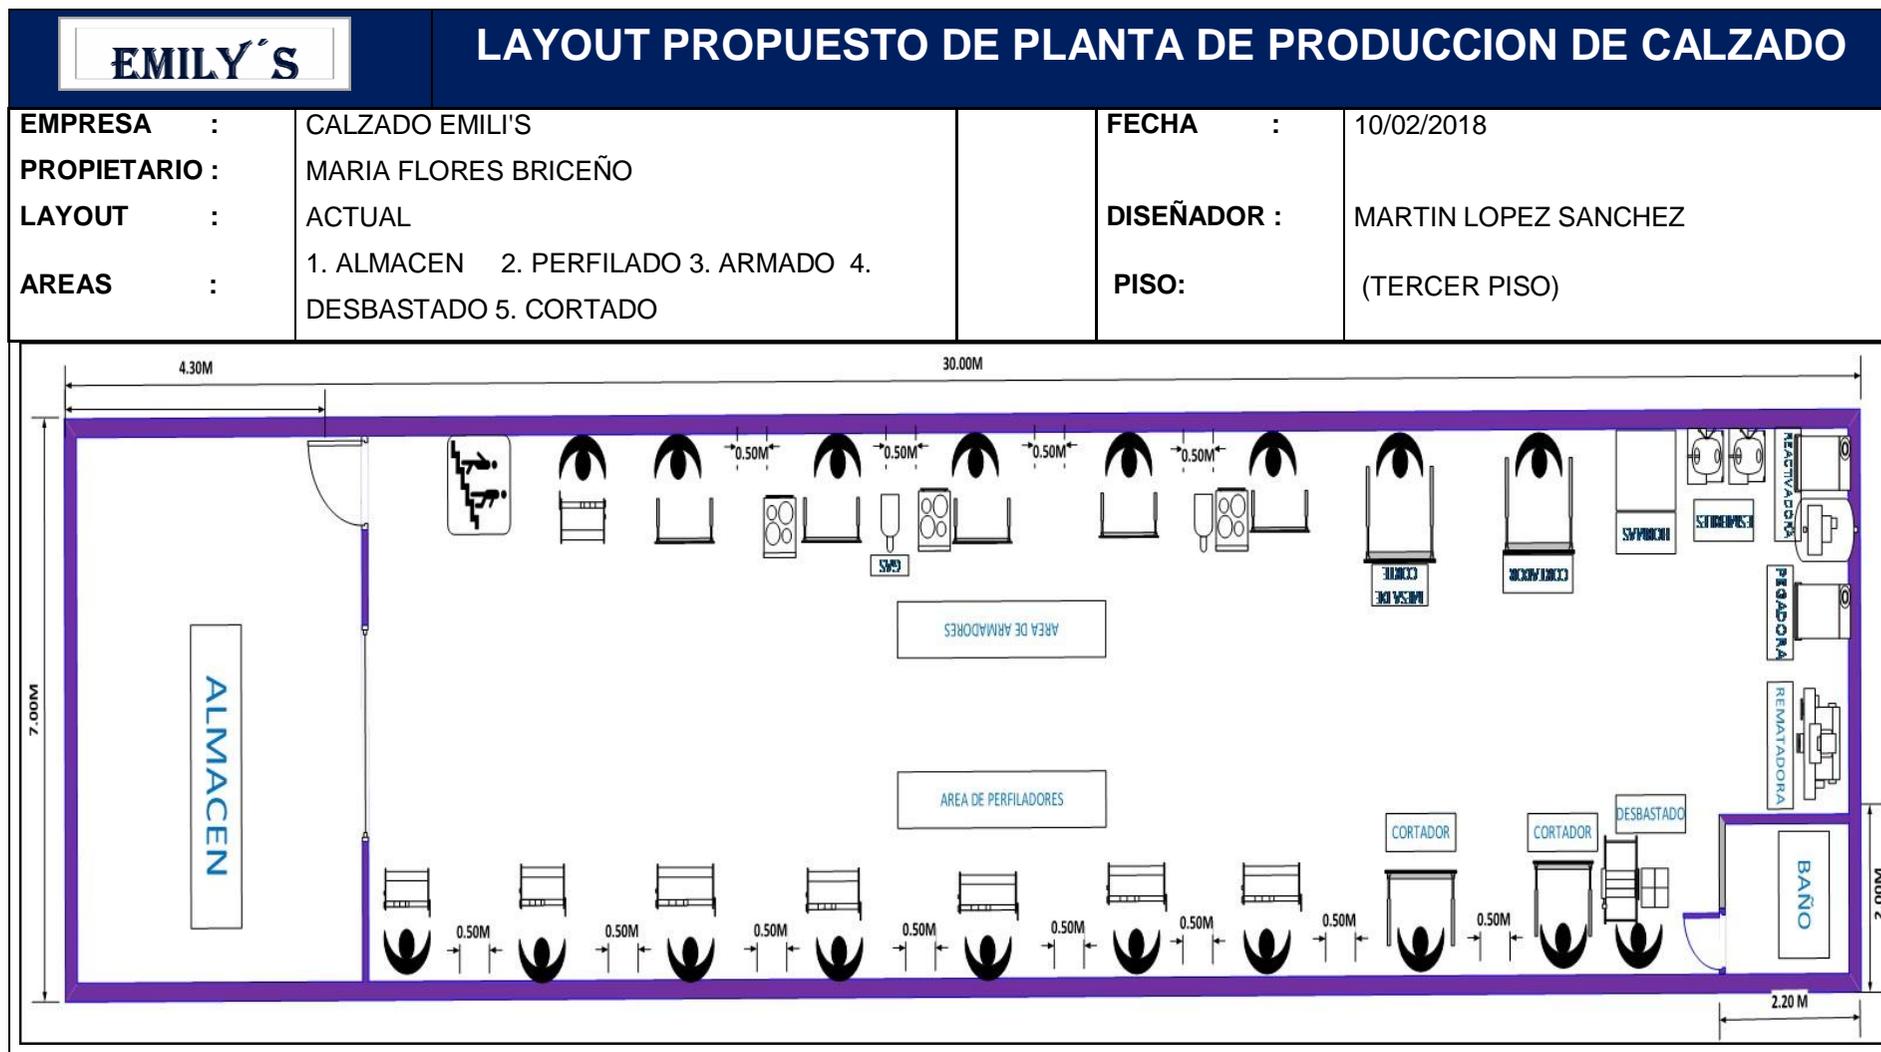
Layout Propuesto de planta para producción de calzado.
